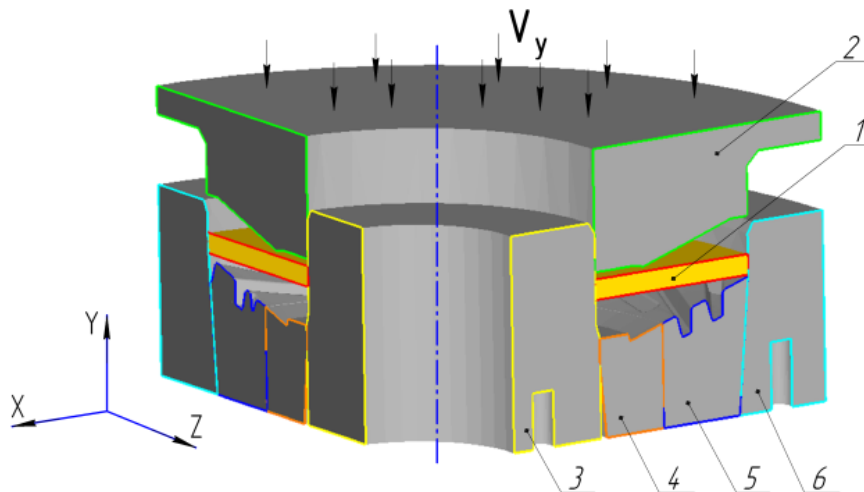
Схема прямого пресування моноколеса з аксіальним розташуванням лопаток:
